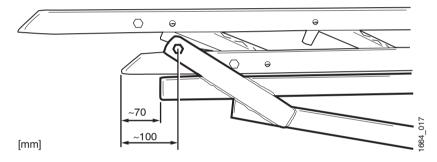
Detalle del extremo inferior de la viga con la escalera añadida
